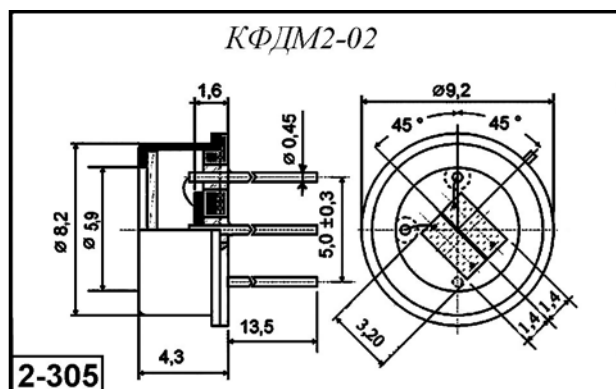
Внешний вид, габаритные размеры кремниевых фотодиодов
